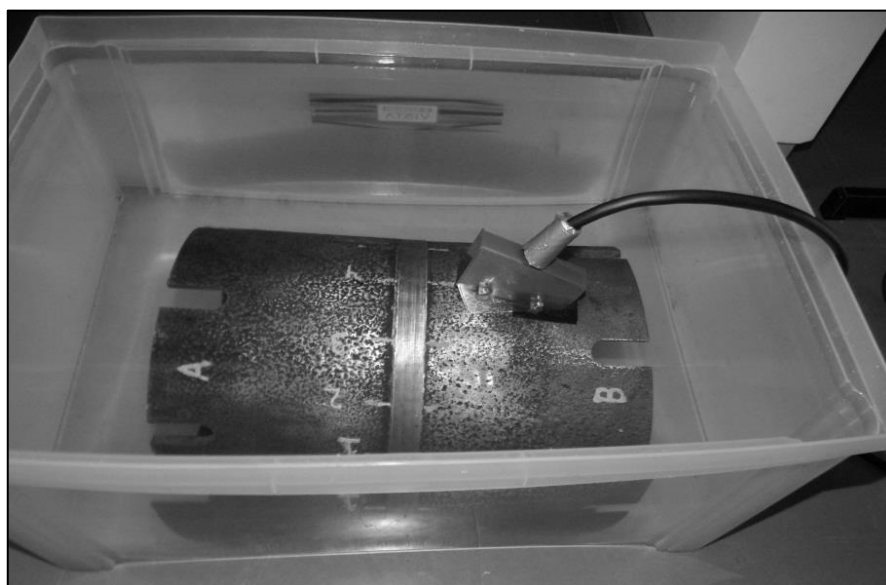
Sensor posicionado sobre a base de ABS inspecionando por imersão o tubo a partir do lado B da solda.
